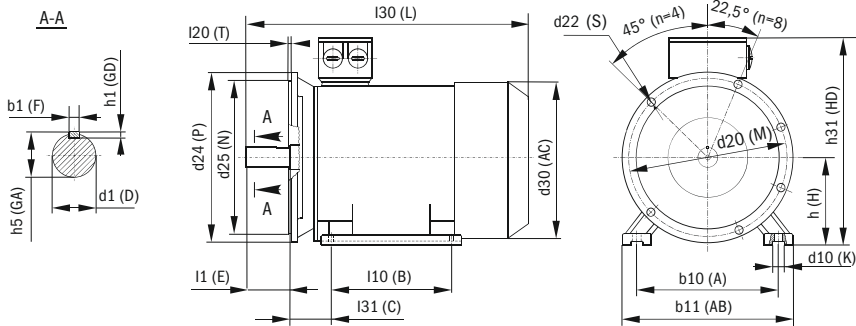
Размеры двигателей монтажного исполнения IM 2181 / Figure 1 – Motor dimensions of IM 2181 mounting version /
